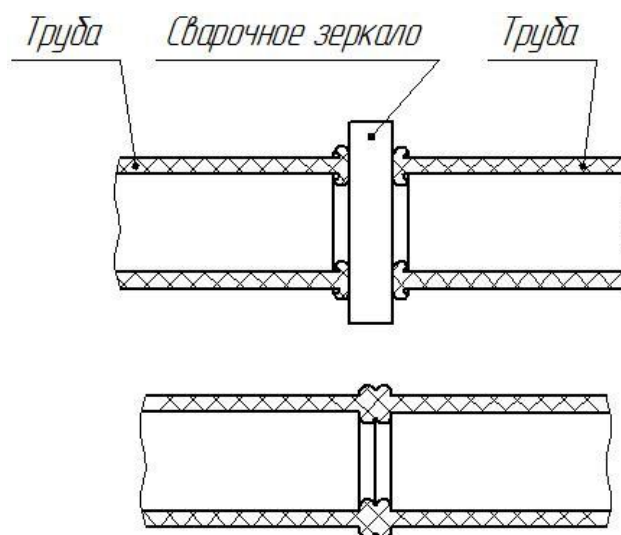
Схема сварки нагретым инструментом встык
